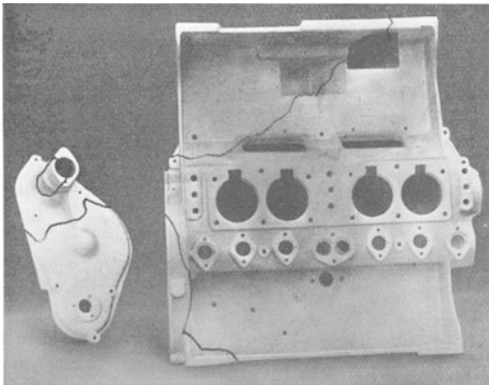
Al-Gehäuse (Abb. 260) fertig geschweißt.
